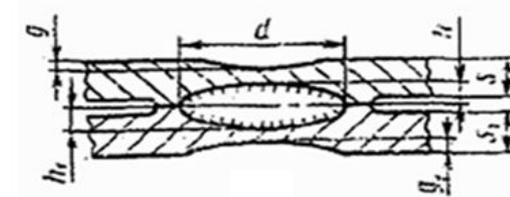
Конструктивные элементы соединения при контактной точечной сварке:
